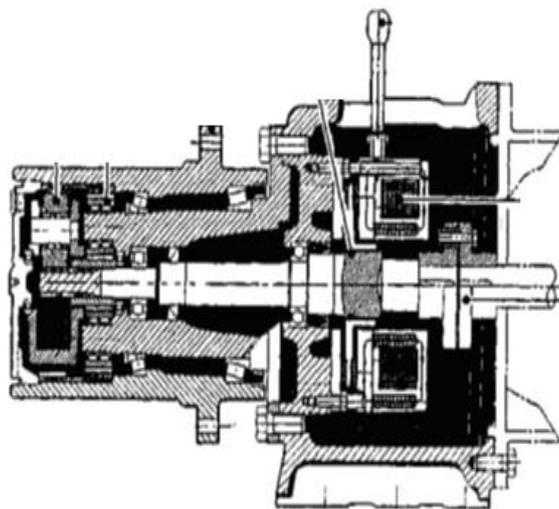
Конструктивная схема лебедки с двухступенчатой планетарной зубчатой передачей
